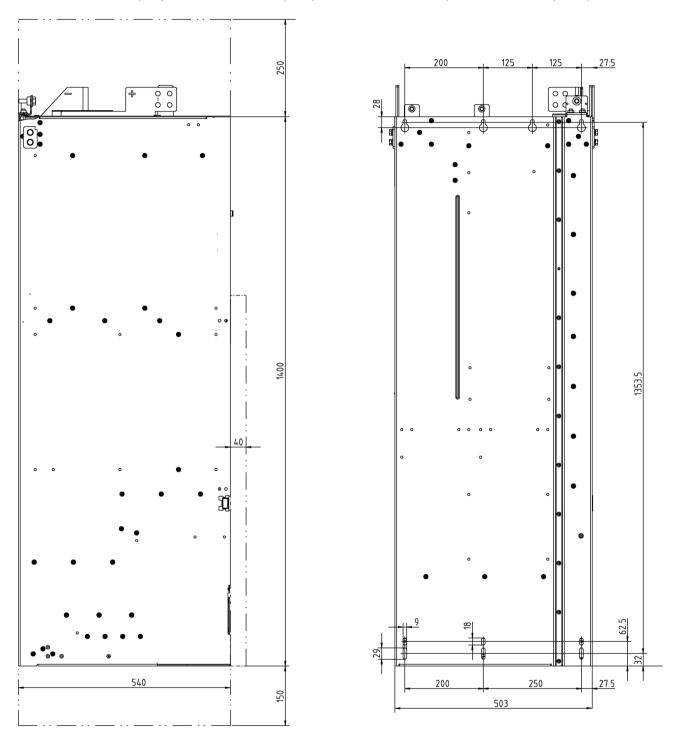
Габаритный чертеж модуля питания Smart, типоразмер НХ. Вид сбоку, вид сзади
